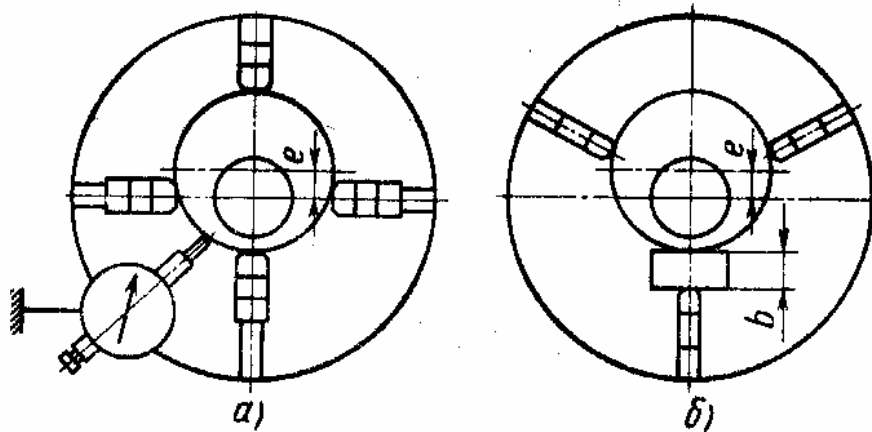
Схеми установлення заготовки зі зсувом в чотири- (а) та трикулачковому (б) патроні при обробці її ексцентричної поверхні
